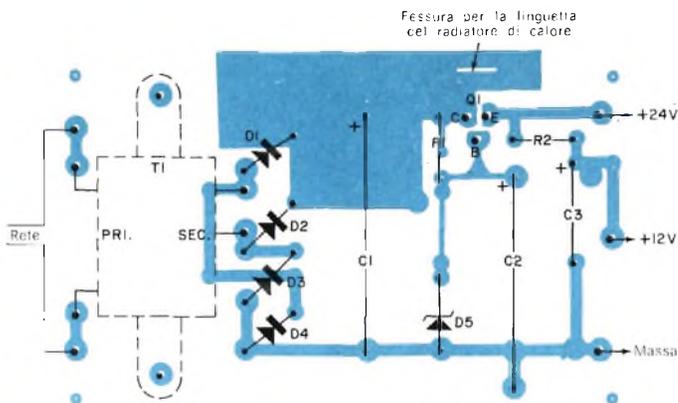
Disposizione dei componenti dell'alimentatore sul circuito stampato. Nel disegno è rappresentato un solo diodo da 24 V (D5).
